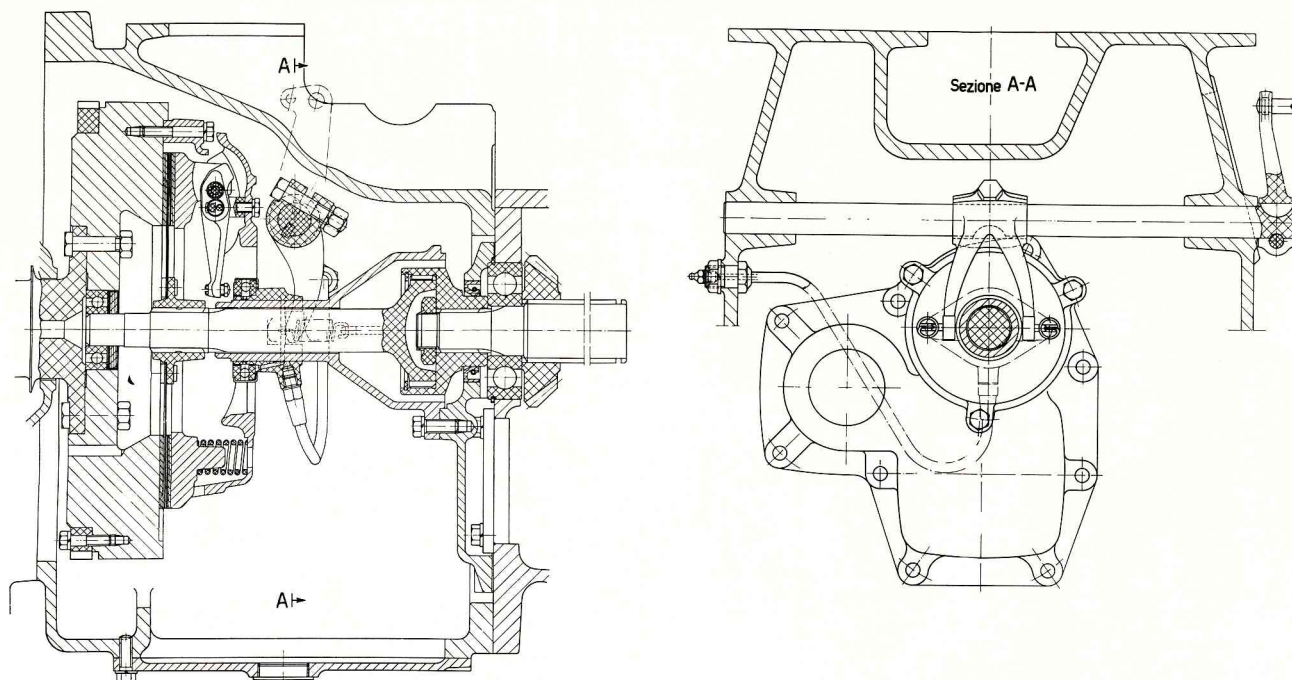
Sezione longitudinale e trasversale della frizione centrale.
